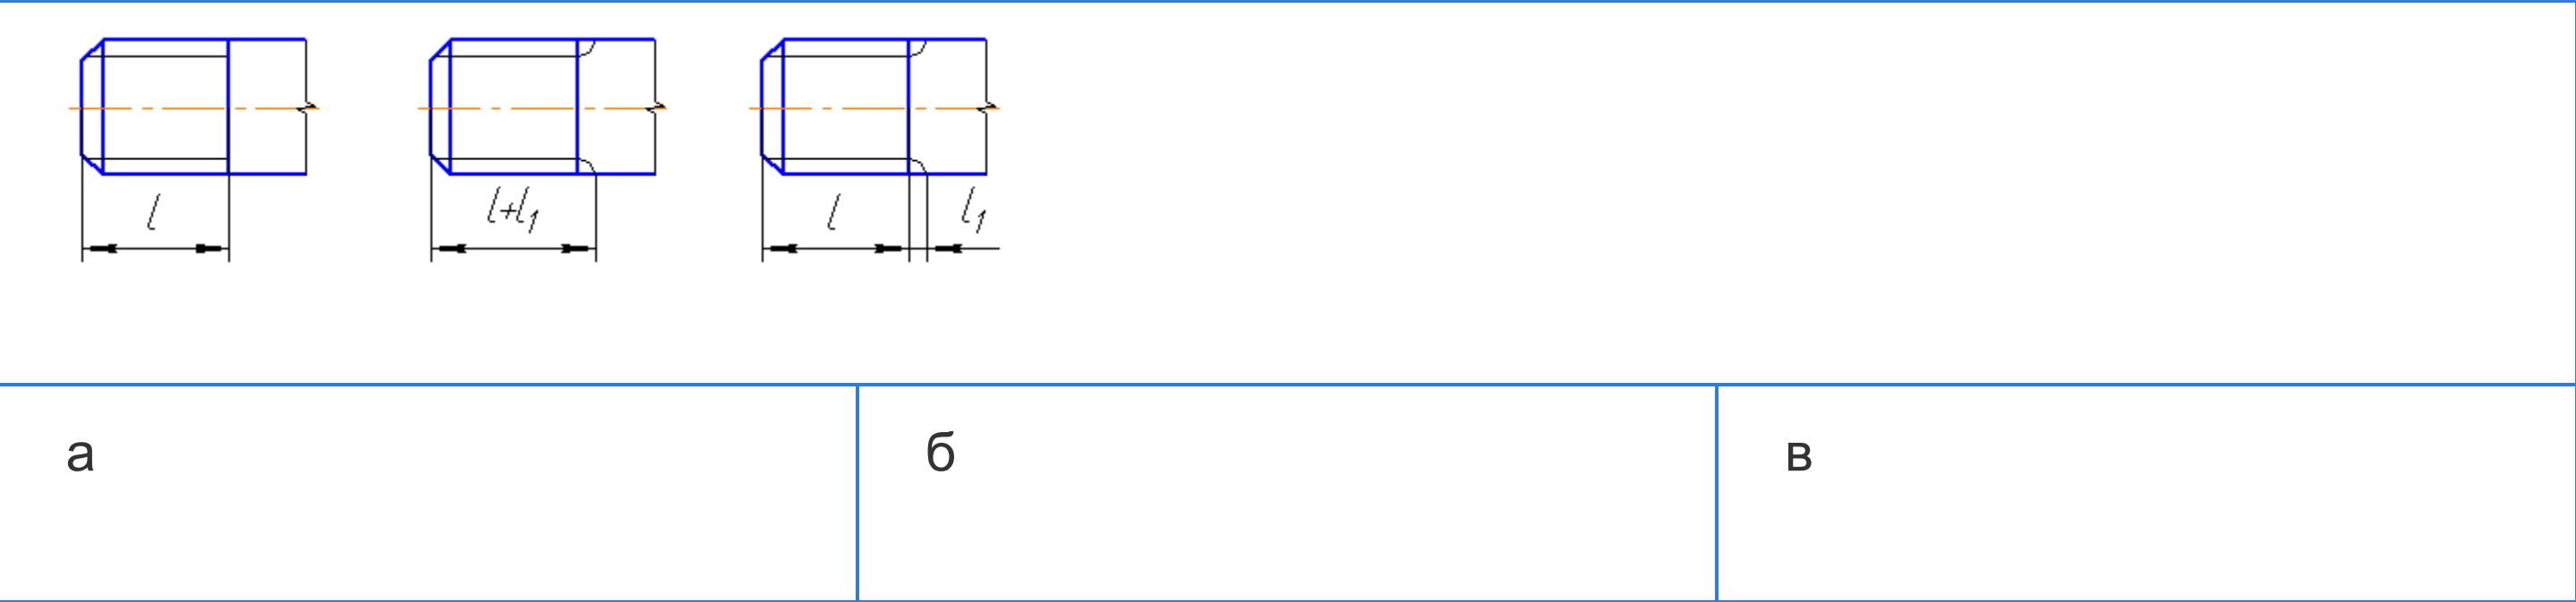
Изображение сбега резьбы, размер длины резьбы
